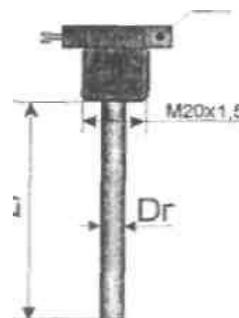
Габаритно-установочные размеры защитной гильзы
